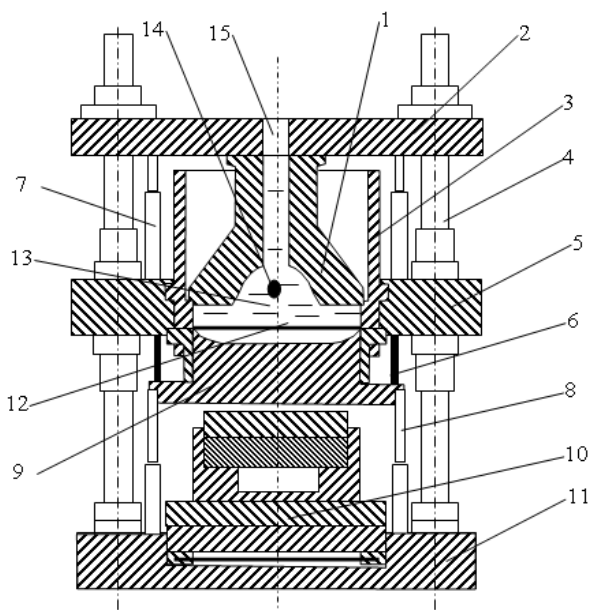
Схема пресса на базе взрывного пресса ВП-2: 1 – камера взрывная; 2 – траверса подвижная; 3 – стакан; 4 – колонны; 5 – траверса неподвижная; 6 – фиксатор; 7 – амортизатор; 8 – цилиндры возврата; 9 – ударник; 10 – технологический блок; 11 – заготовка; 12 – эластичная диафрагма; 13 – вода; 14 – заряд БВВ; 15 – отверстие.
